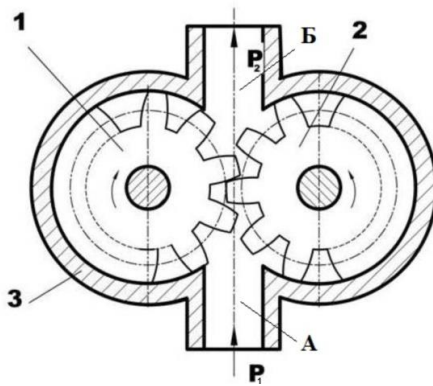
Схема шестереного насоса: 1 – ведуче зубчасте колесо (шестерня); 2 – ведене зубчасте колесо; 3 – корпус із порожнинами: всмоктування А і нагнітання Б
